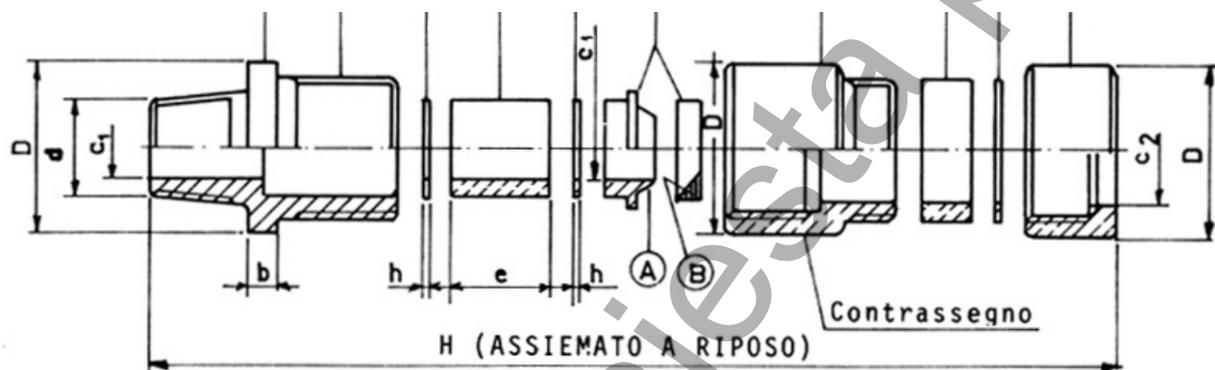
B – Esempio di pressacavo per cavo armato
